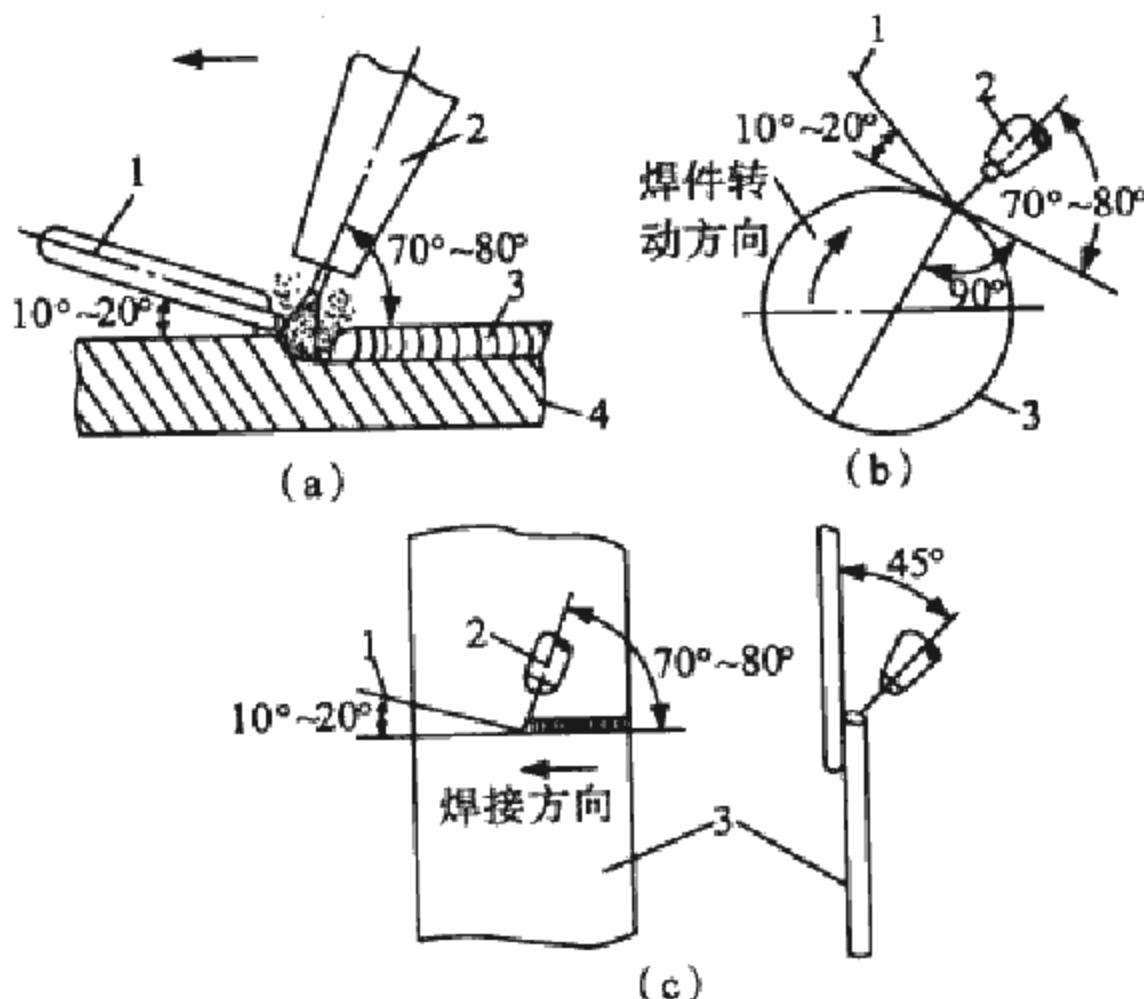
手工钨极氩弧焊焊接纯铜平焊缝时的焊枪、焊丝和焊件的相对位置
